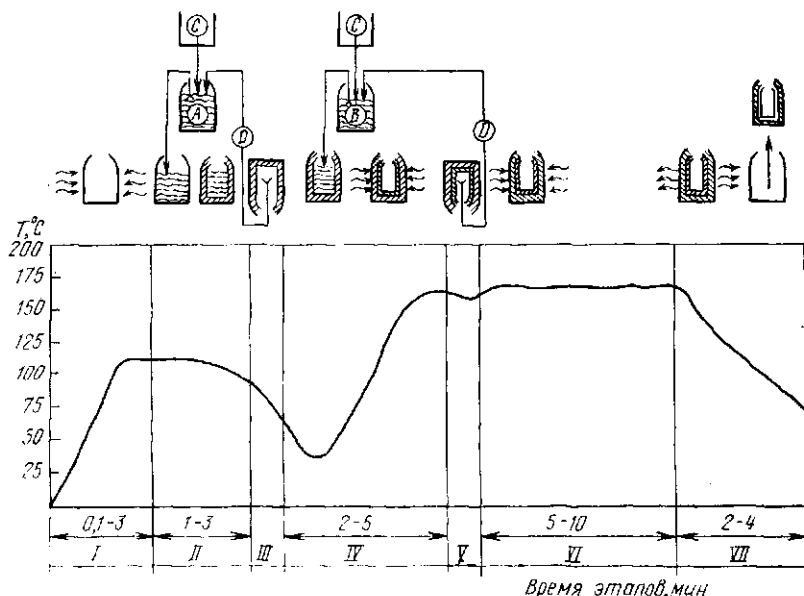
Схема литья с опрокидыванием (изготовление корпуса сумки)
